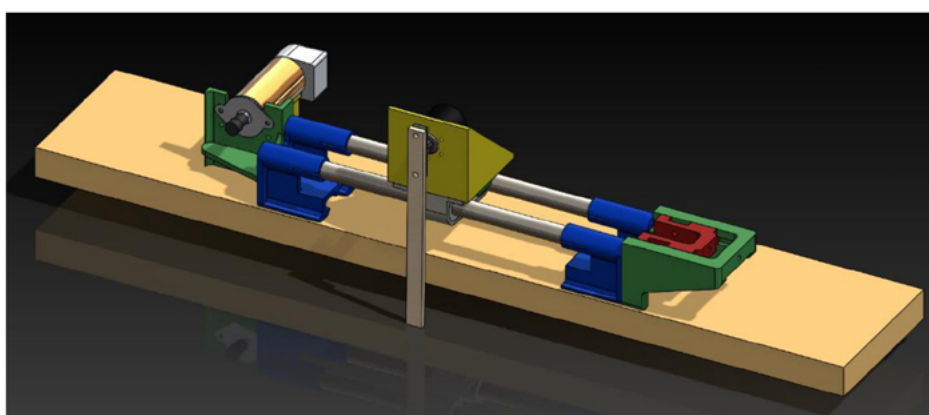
Modelo CAD de las partes principales del sistema carro péndulo construido.
